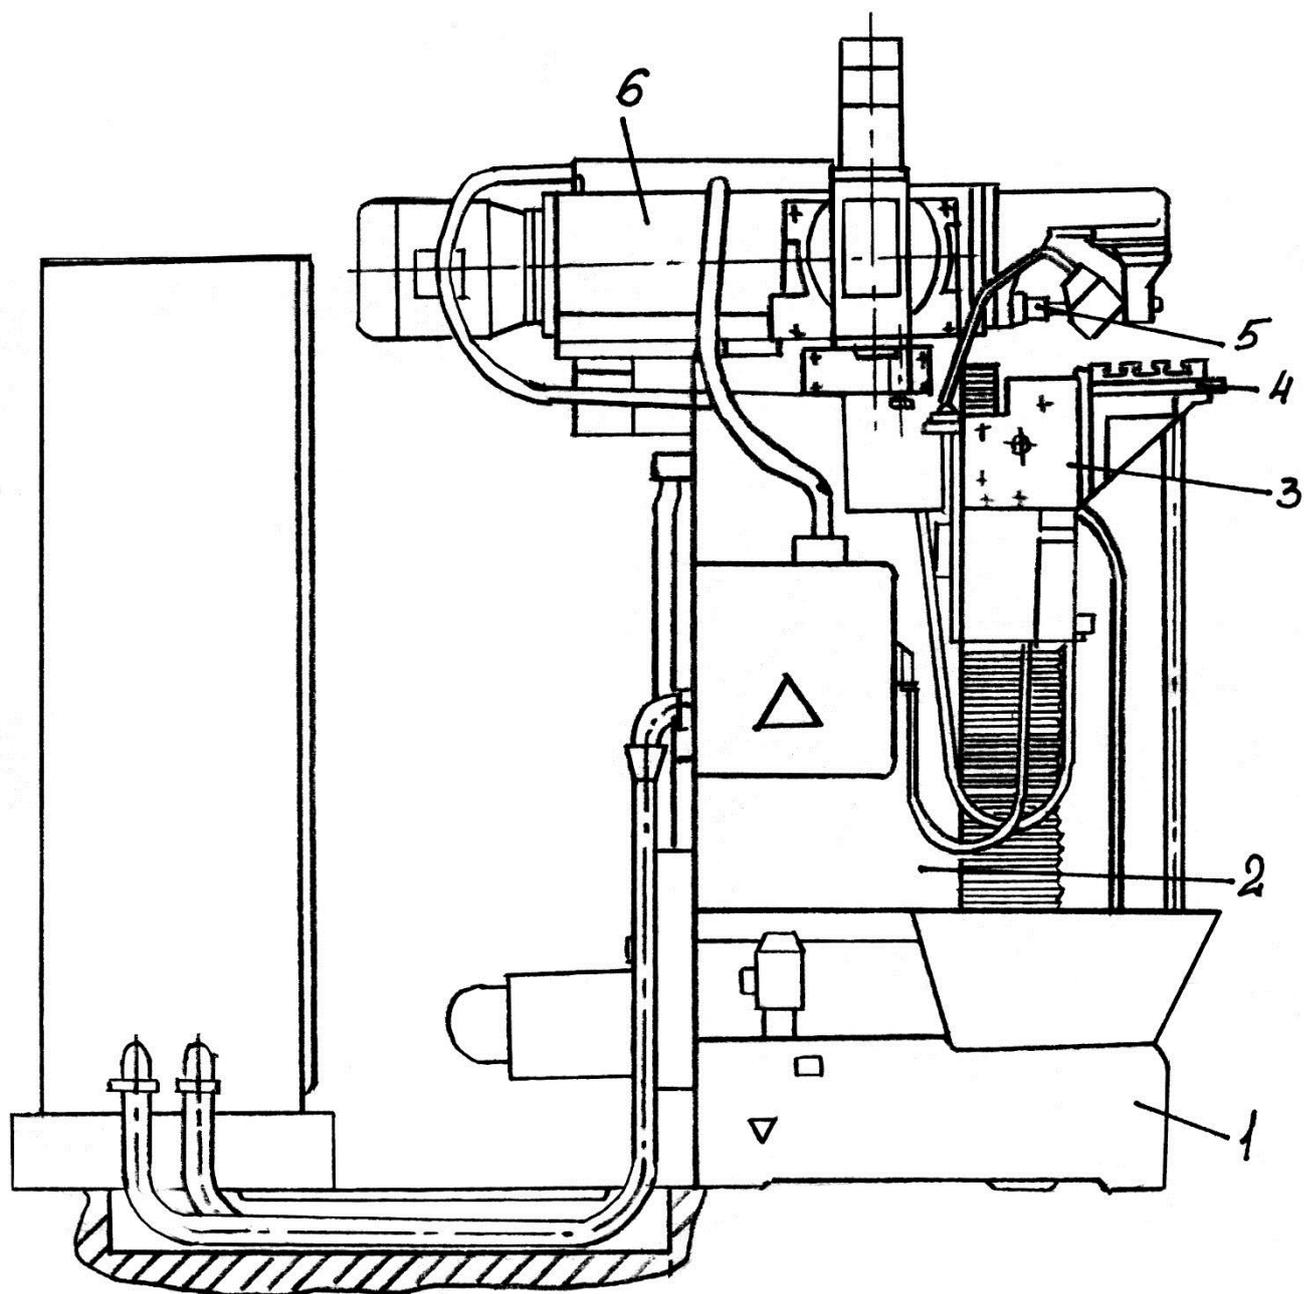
Основные узлы станка мод 6720ВФ2
